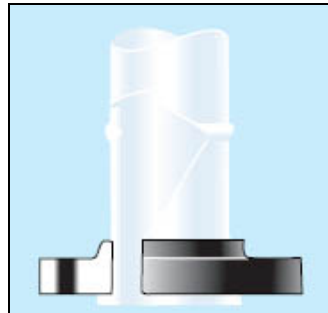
BRIDA PARA JUNTA CON SOLAPA [18].
